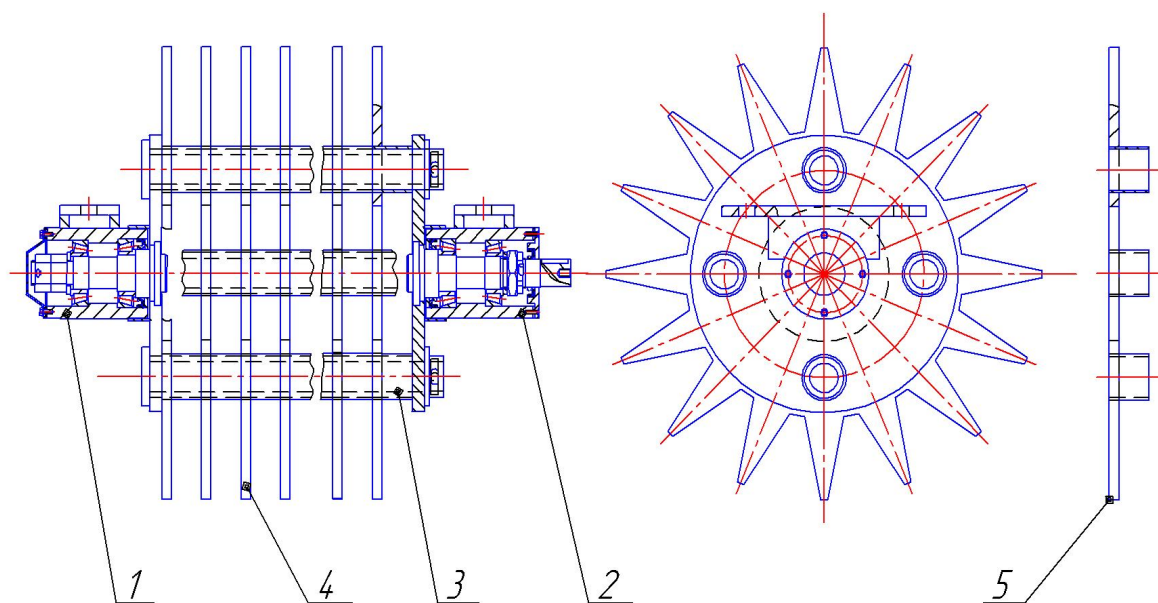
Задний ротор: 1 – опорный узел; 2 – опорно-приводной узел; 3 – дистанционная втулка; 4 – зубчатый диск; 5 – зубчатый диск с приваренными втулками
